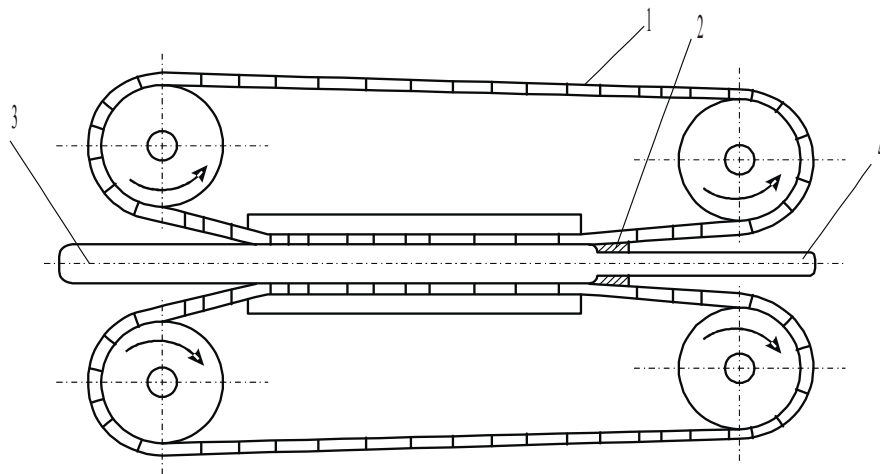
Схема безперервного пресування способом Лайнекс: 1 - приводні ланцюги, 2 - матриця, 3 - заготовка, 4 - виріб
